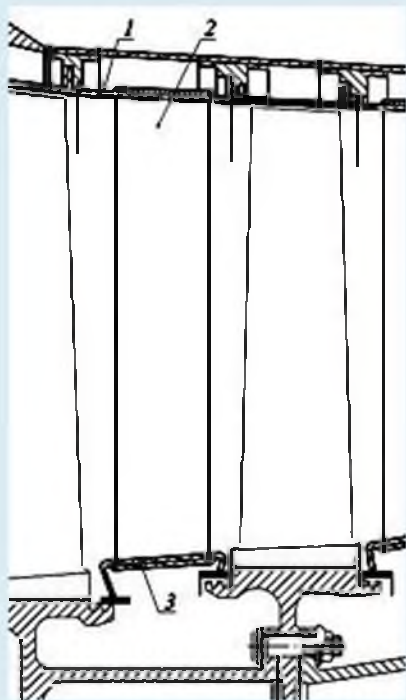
Статор компрессора ТВаДТВ2-117с двухпорным НА
